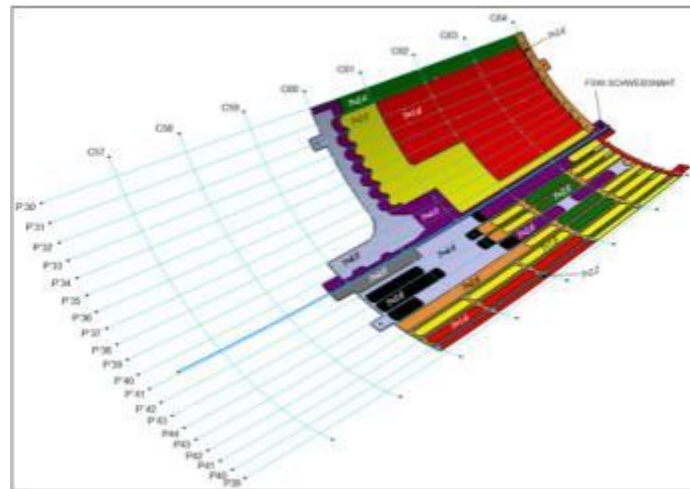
Beplanktes Hautfeld mit jeweiliger Blechstärke
